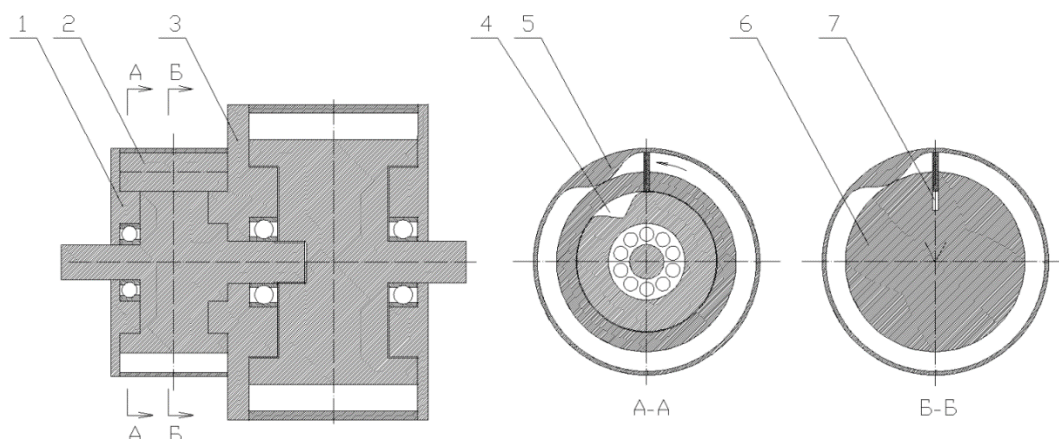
Конструкция роторно-лепестковых камер сжатия и расширения
